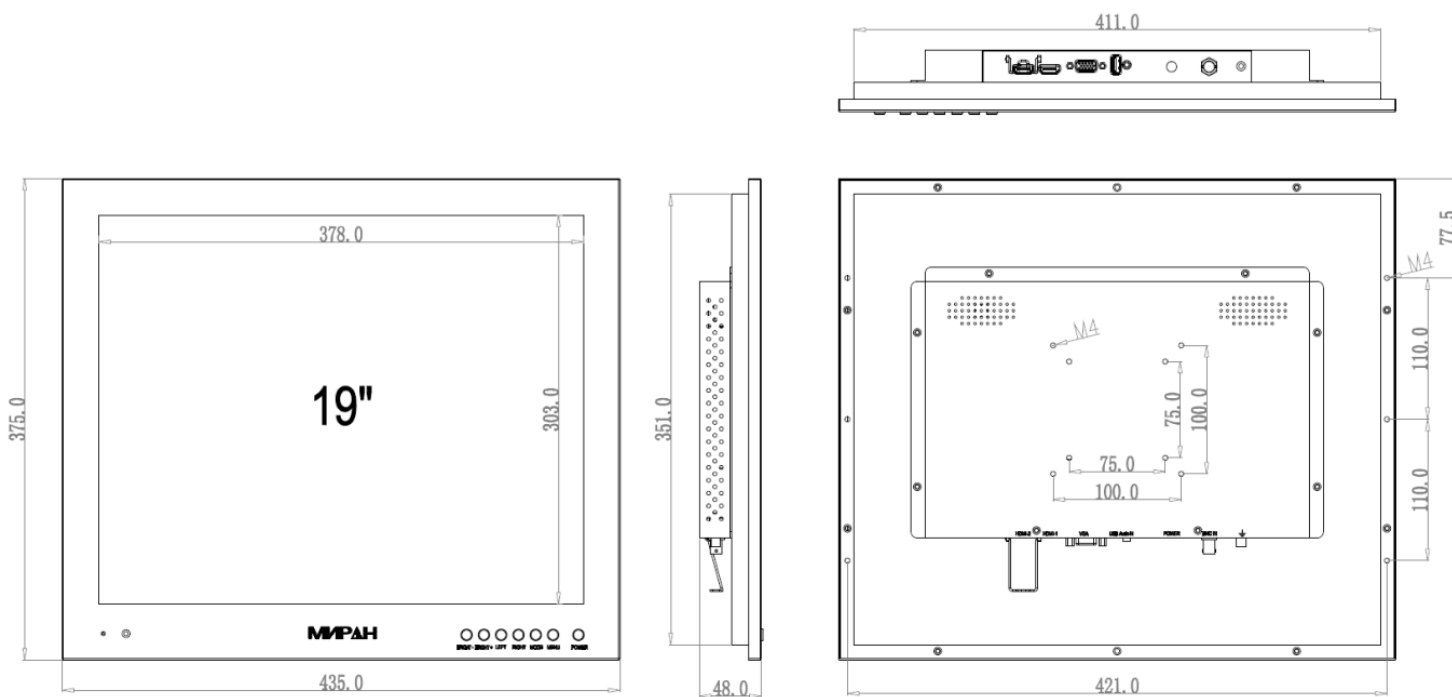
Габаритный чертеж монитора ИВМ-19ЖК.
